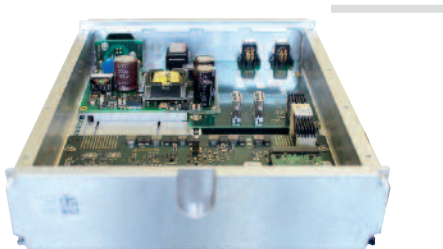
Компоновка внутри корпуса компьютера BC50R
